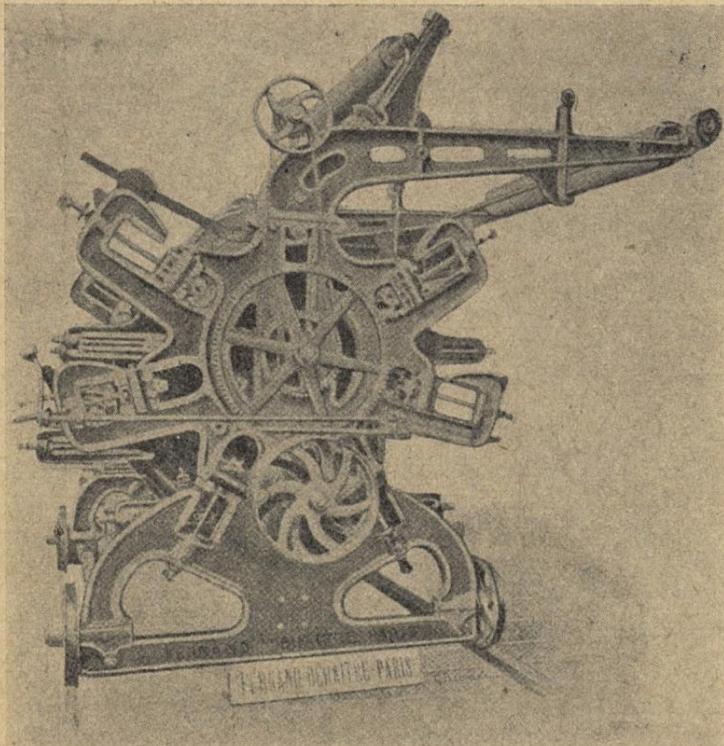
Machine à imprimer la toile cirée à 6 couleurs.
